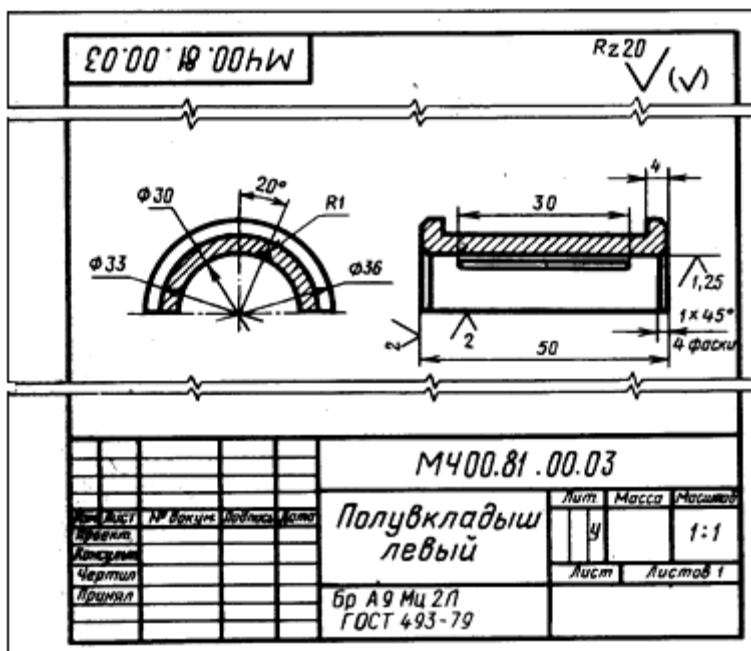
Пример рабочего чертежа крышки полувкладыша левого
